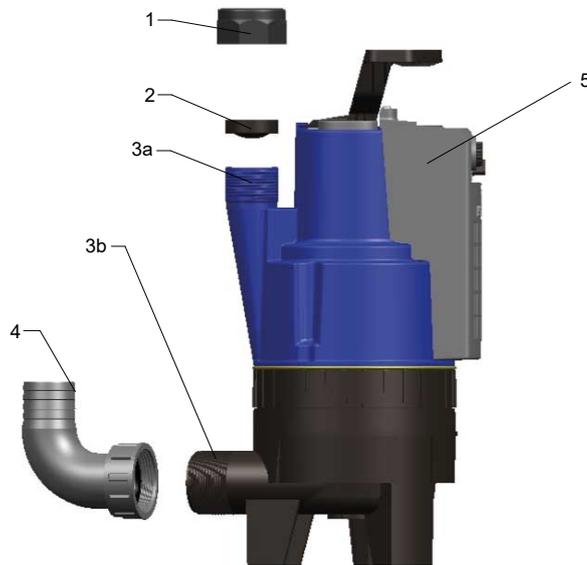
Pumpenaggregat entleeren / reinigen, Baugröße 354
